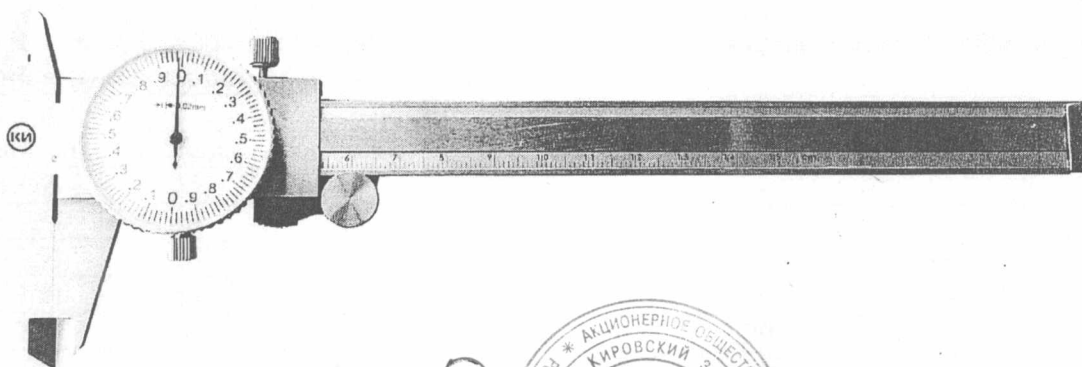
Общий вид штангенциркулей типа ШЦК-I
